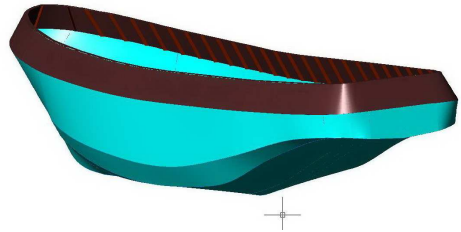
3D-модель наружной обшивки и фальшборта в ShipConstructor.
